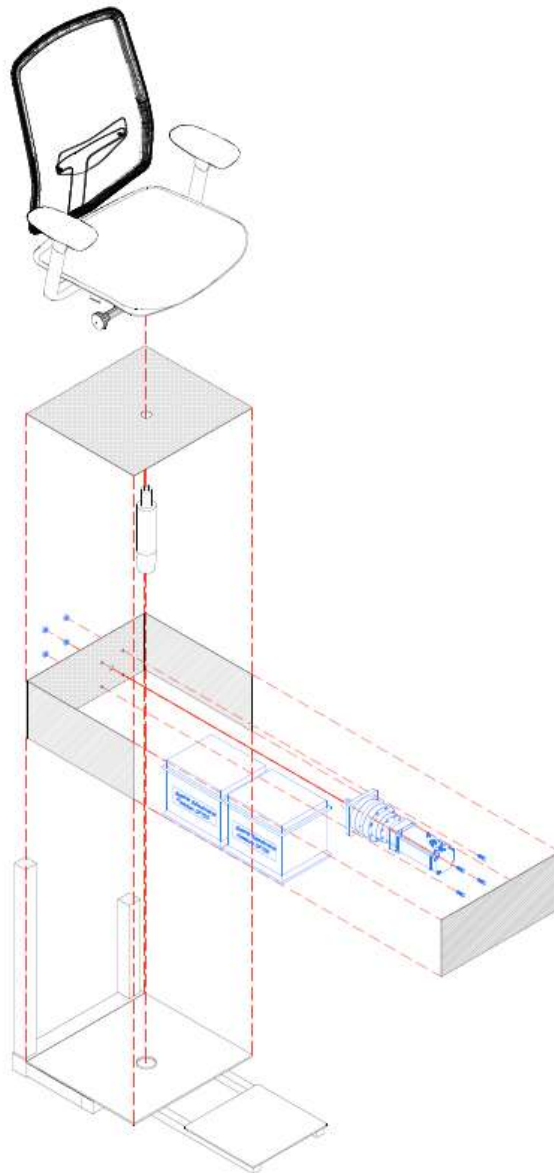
Montagem final, com os componentes da cadeira elevatória integrados em conjunto
